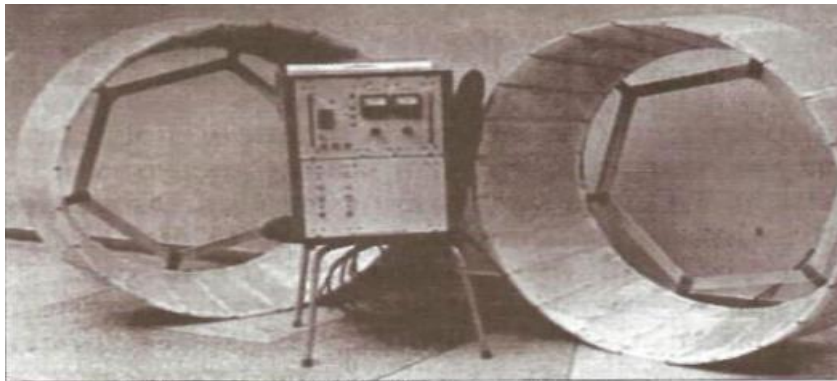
Індукторна установка для нагрівання коліс
